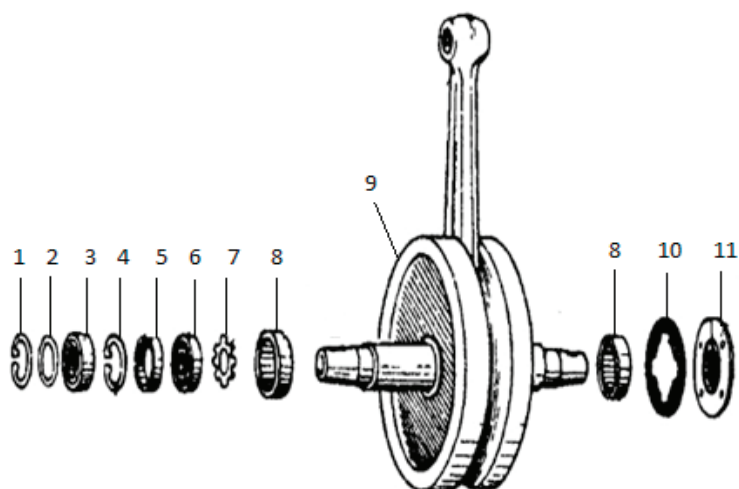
Кривошипно-шатунный механизм двигателя Иж Планета 5
